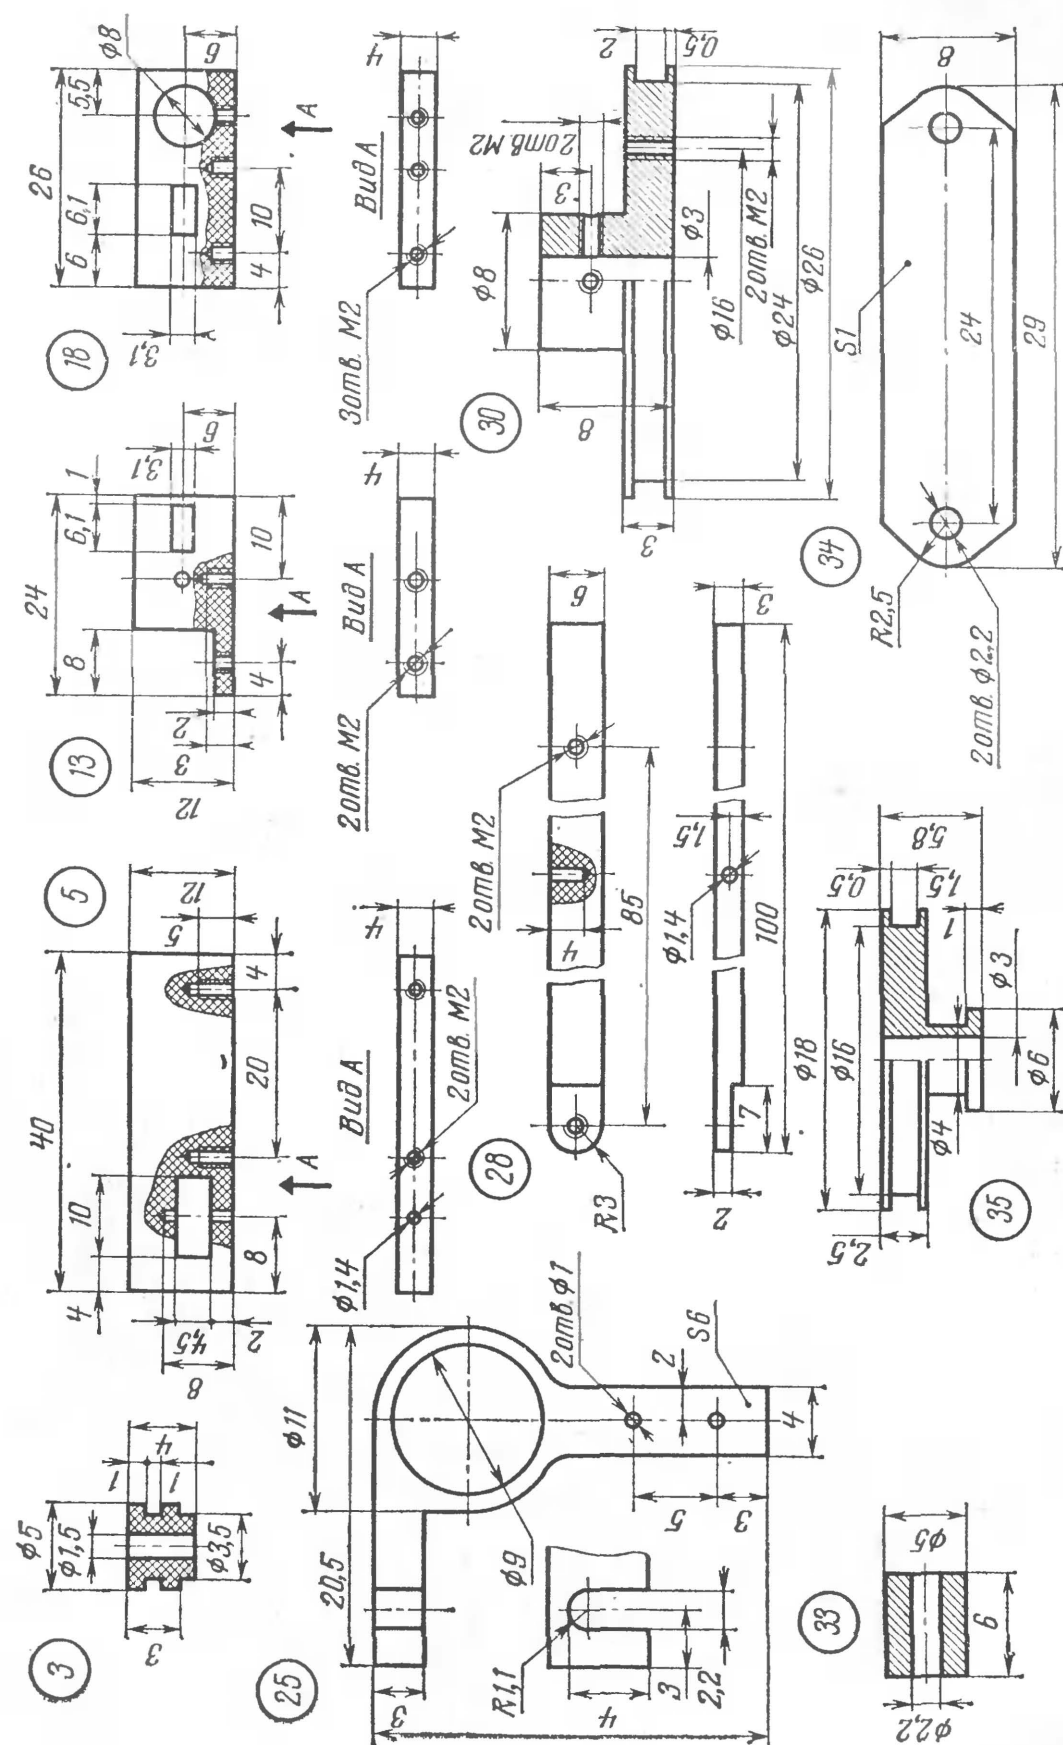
Детали механизма сопряжения: 3 — ролик; 5 — кронштейн шкального устройства; 13 — кронштейн малый; 18 — кронштейн; 25 — держатель катушки; 28 — шток, гетинакс; 30 — шкив верньерного устройства; 33 — стойка; 34 — планка, ЛС59-1; 35 — шкив. Материал дет. 3, 5, 13, 18 и 25 — стекло органическое; 30, 33, 35 — дюралюминий Д16-Т
